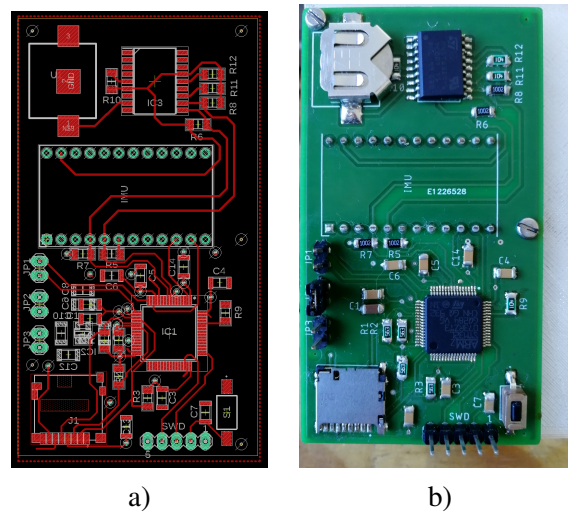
a) Desenho da placa utilizando o EAGLE b) Placa final completamente montada
